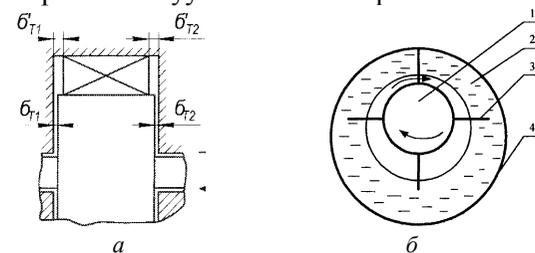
Схемы зазоров и щелей вакуумного насоса: а – пластинчатый (b_{T1} , b_{T2} – торцовые зазоры; b'_{T1} , b'_{T2} – торцовые зазоры между лопаткой и боковыми крышками); б – водокольцевой (1 – ротор; 2 – жидкостное кольцо; 3 – лопатки; 4 – корпус)
